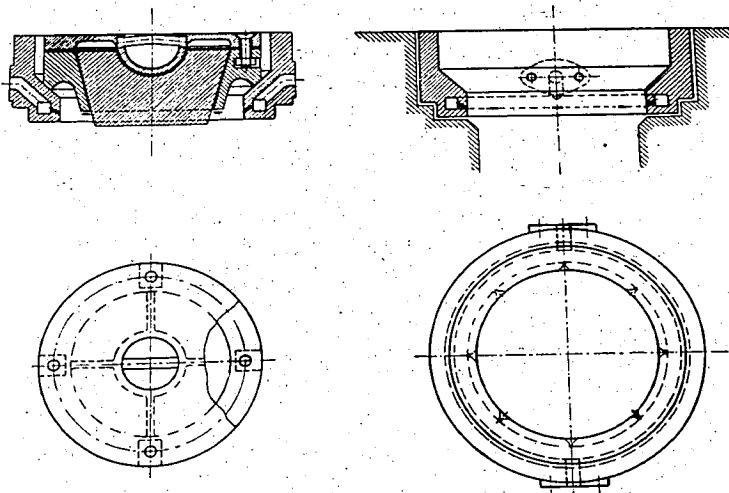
Didier-Fülldeckel mit Dampfkranz.
